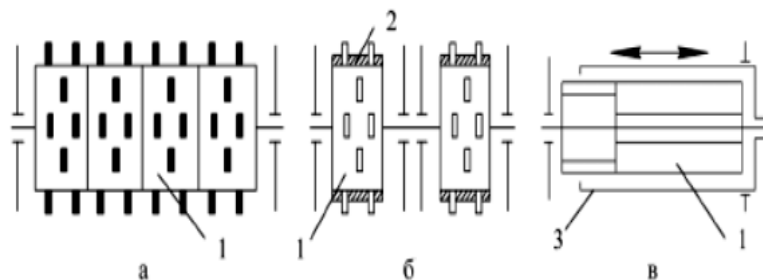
Конструкции дозирующих устройств катушечного типа:
